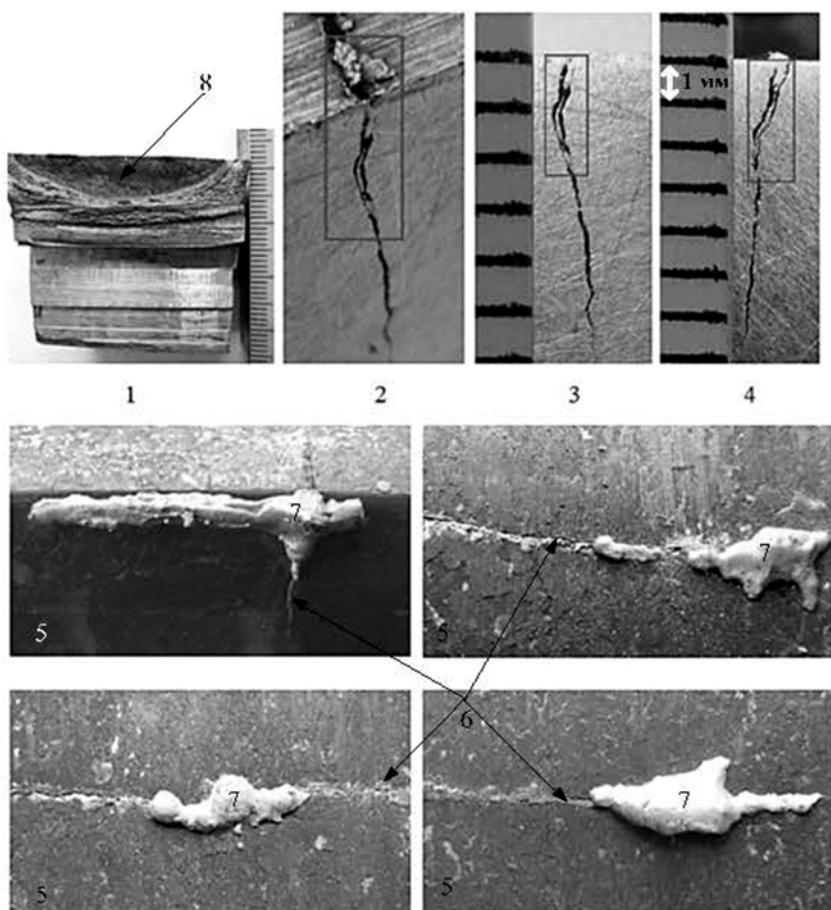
Характер розташування поперечних тріщин, що утворюються на робочій поверхні розливального колеса та фрагменти безперервнолитої мідної заготовки. 1 – розріз колеса в місці утворення поперечної тріщини; 2 – 4 – глибина проникнення тріщини; 5 – робоча поверхня розливального колеса; 6 – тріщини; 7 – фрагменти відірваної безперервнолитої мідної заготовки; 8 – графітове мастило на поверхні тріщини.
